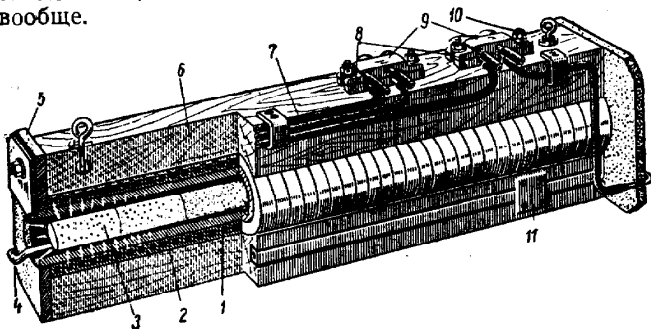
Индуктор для нагрева цилиндрических заготовок:
